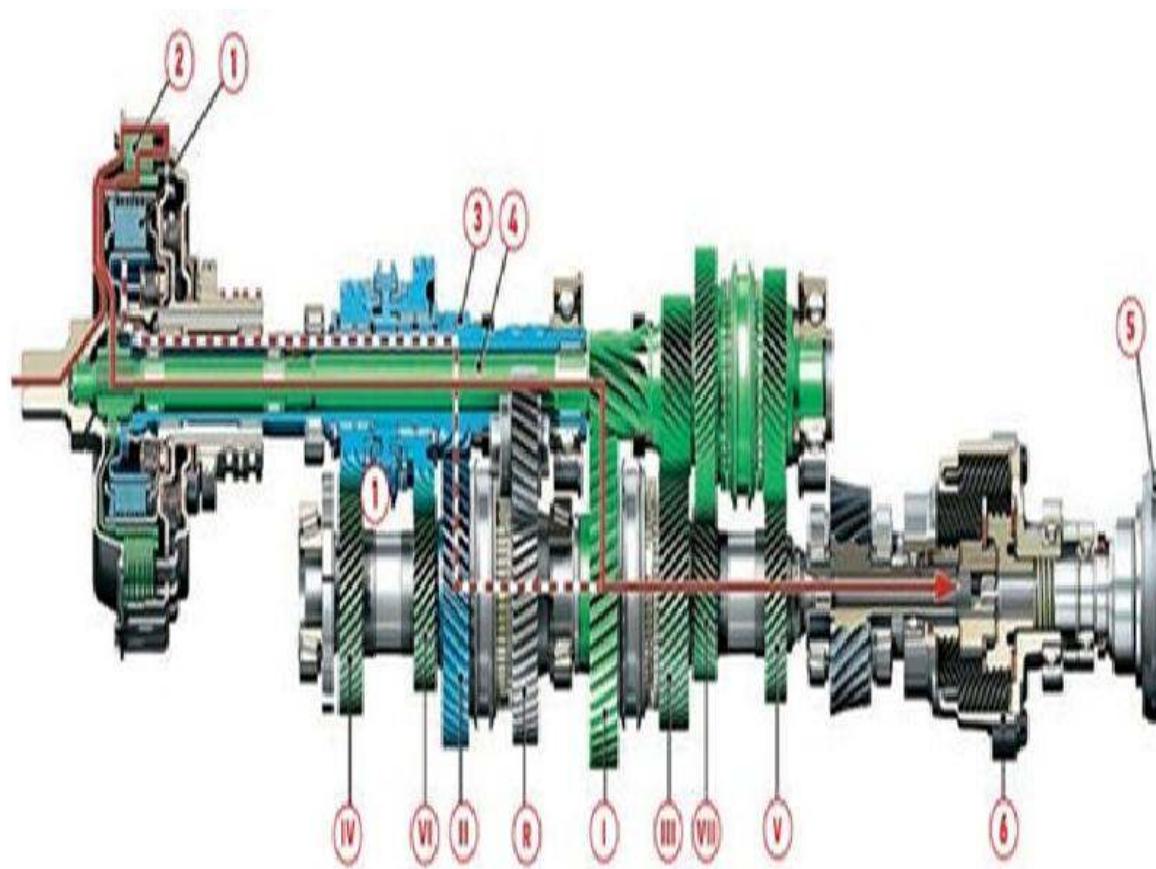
Схема трехвальной коробки передач с двойным сцеплением:
